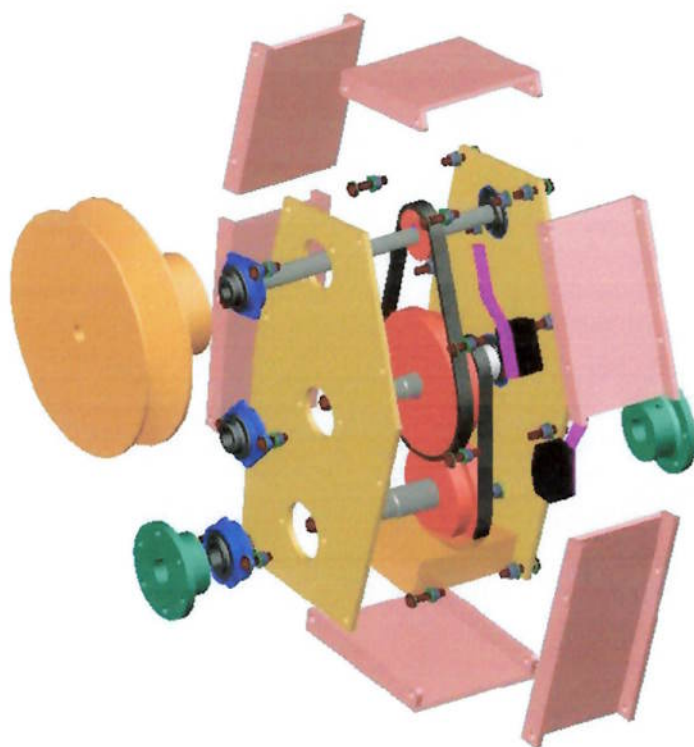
Vista explodida da caixa de transmissão de 2004
